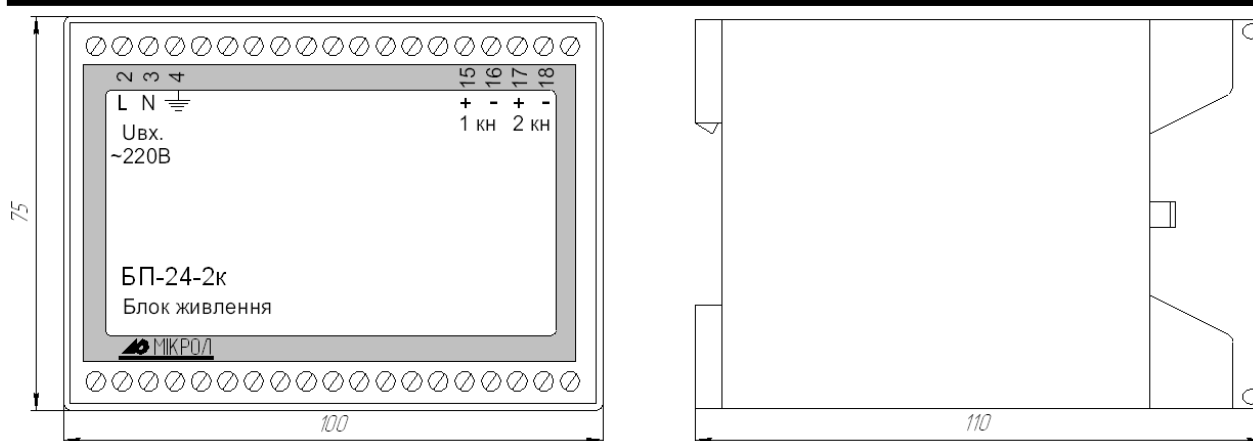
Зовнішній вигляд та габаритні розміри блока живлення
